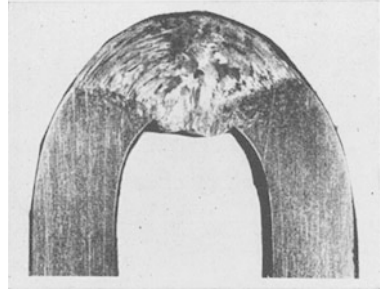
Aluminiumbronzeschweißung, um 180° gebogen.
